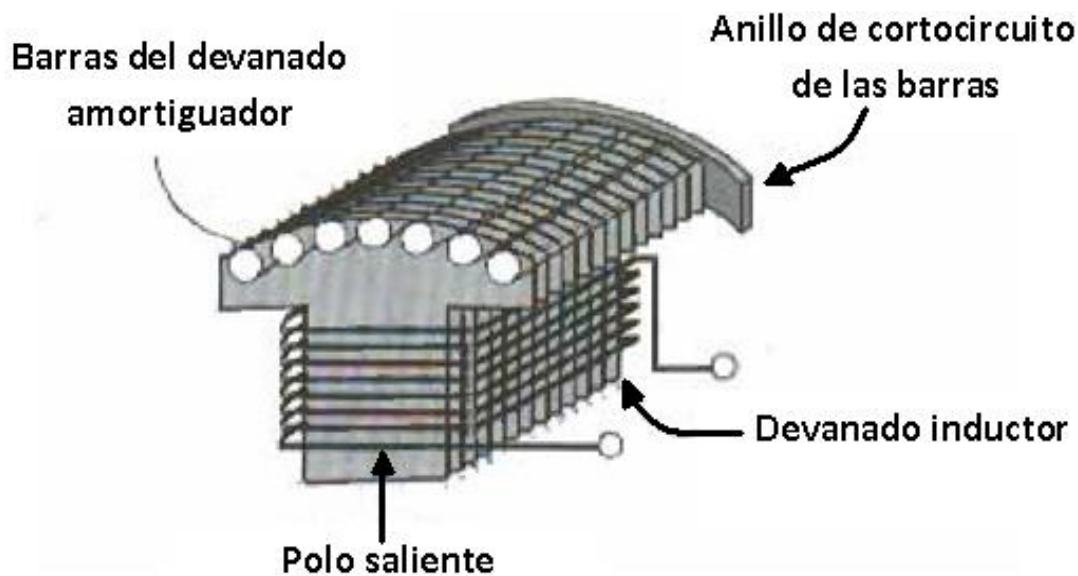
Devanado de amortiguamiento colocado en los polos del rotor de un motor síncrono (Fuente: [3])
